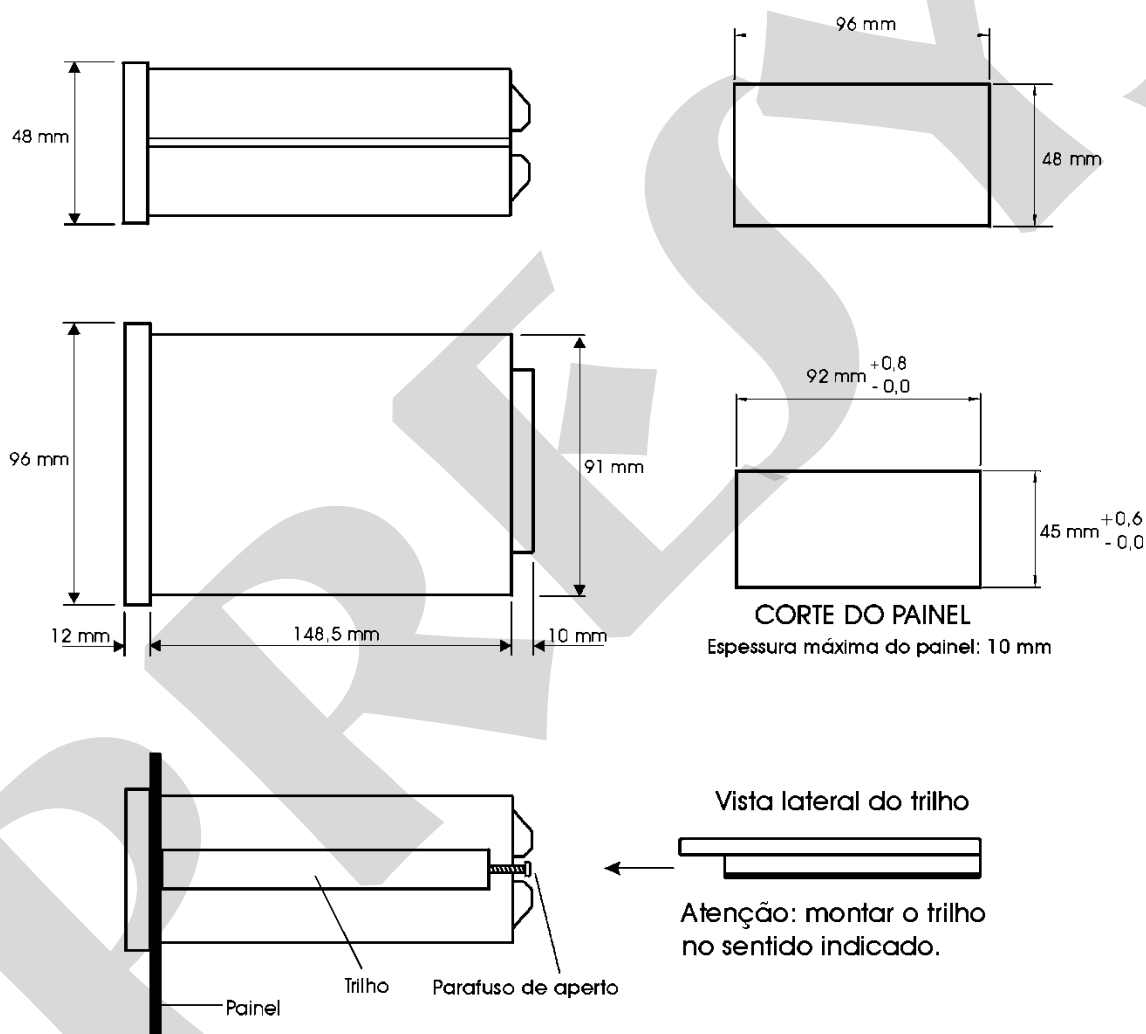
Desenho dimensional, corte e vista lateral da montagem no painel
